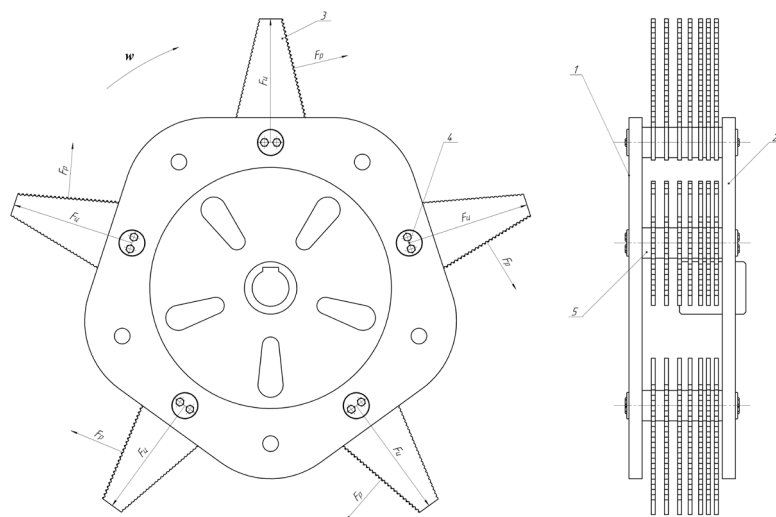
Схема ротора мобильной установки для переработки древесной зелени хвойных пород в хвойно-витаминную муку: 1 – передняя крышка ротора; 2 – задняя крышка ротора; 3 – нож, приваренный к ступице; 4 – концевая шайба; 5 – ось; F_p – сила резания, Н; $F_{ц}$ – центробежная сила, Н; ω – угловая скорость, с⁻¹
